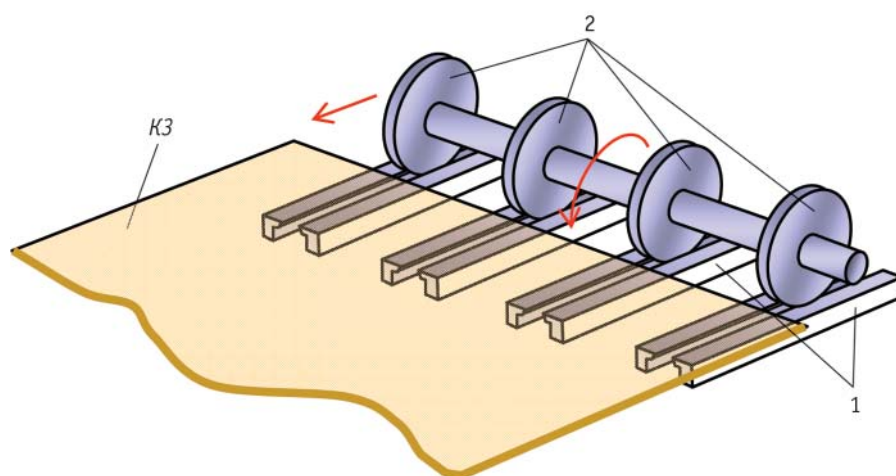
Схема виготовлення пазів у великоформатній картонній заготовці ножичним різанням дисковими інструментами
